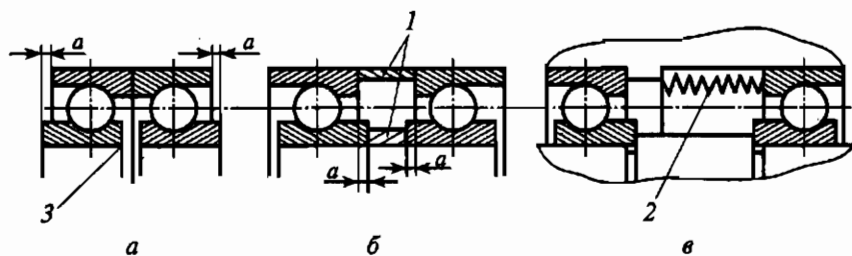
Способы создания предварительного натяга радиально-упорных шарикоподшипников:
